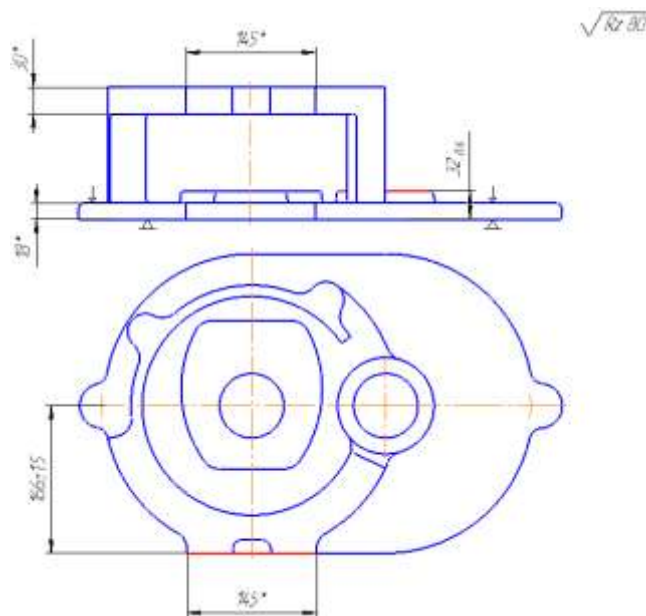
Эскиз к операции 15 – Фрезерная
